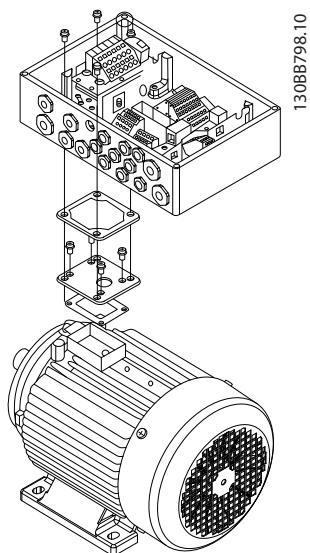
Montaje del motor FCD 302 con una placa adaptadora.
